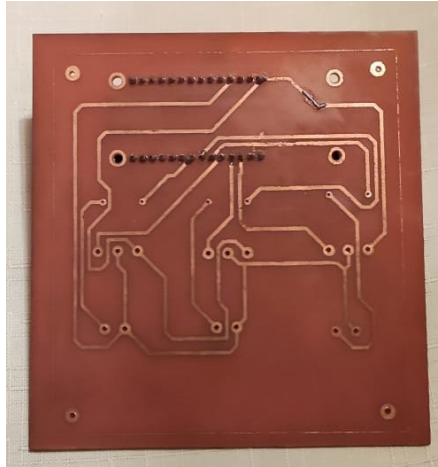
Layout PCB para su posterior impresión. (Fuente: Autor)
